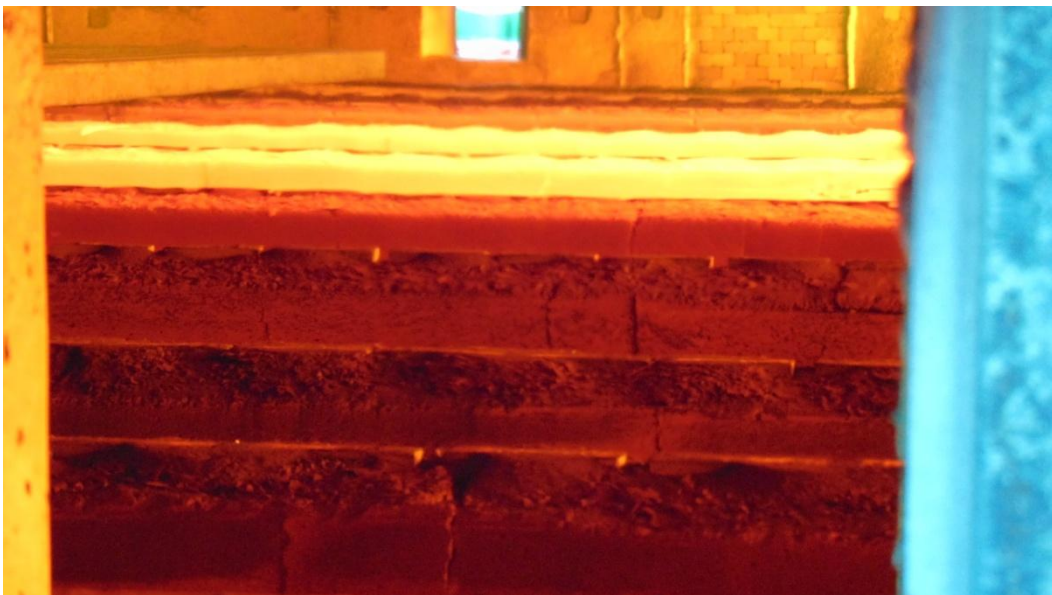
Zona de enformamento tipo walking beam (acrescento 2004)
